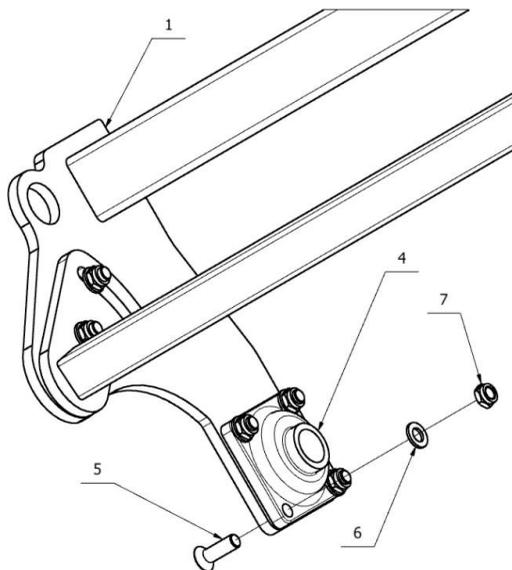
Gummiwelle Ø500mm - Lagermontage.
